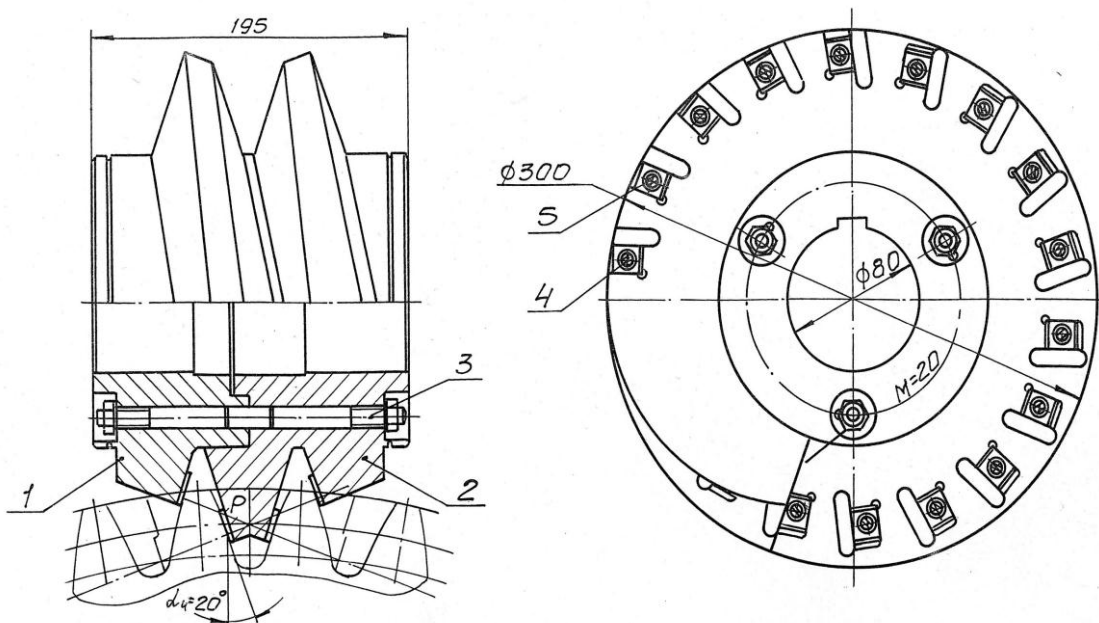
Схема однокорпусной фрезы двухстороннего резания, состоящей из 2-х одновитковых корпусов
